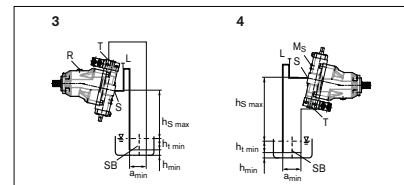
Übertankeinbau mit Einbaulage 3–4
